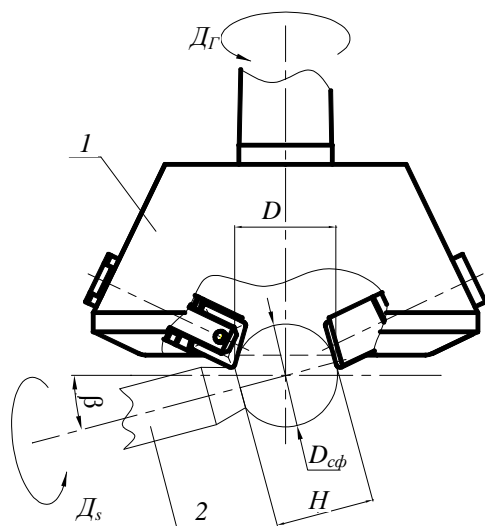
Охватывающее фрезерование сферической поверхности детали
